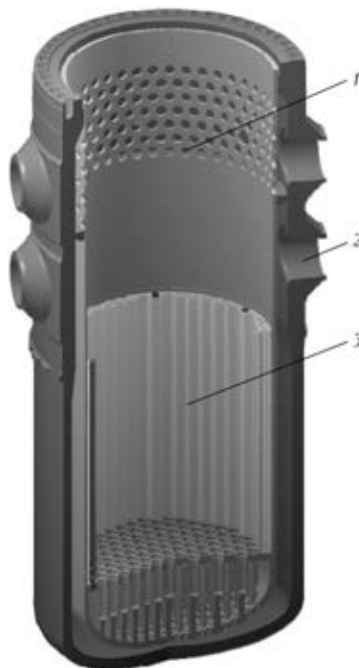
Конструкция реактора: 1 — шахта; 2 — корпус; 3 — выгородка
